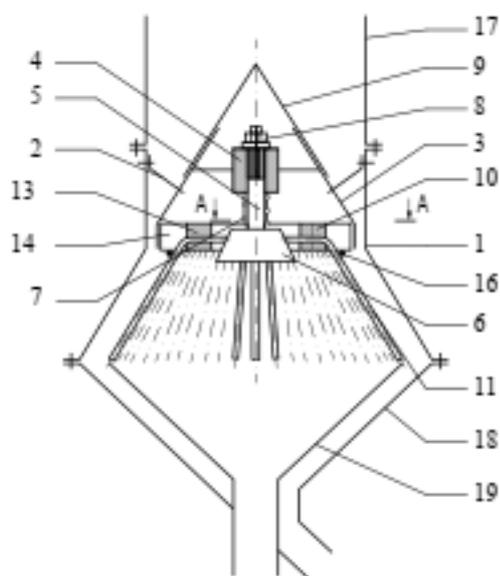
Сепаратор з конічною поверхнею: 1 – корпус; 2 – кронштейн; 3 – тримач; 4 – напрямні утримувача; 5 – вал; 6 – регулюючий конус; 7 – пружний елемент; 8 – гайка; 9 – розподільний пристрій; 10 – втулка; 11 – вигнуті рухомі стрижні; 12 – нерухомі стрижні; 13 – отвори; 14 – вертикальні пази; 15 – похилі отвори; 16 – кільцевий пружний елемент; 17 – приймальний пристрій; 18 – приймач сходової фракції; 19 – приймач прохідової фракції.
